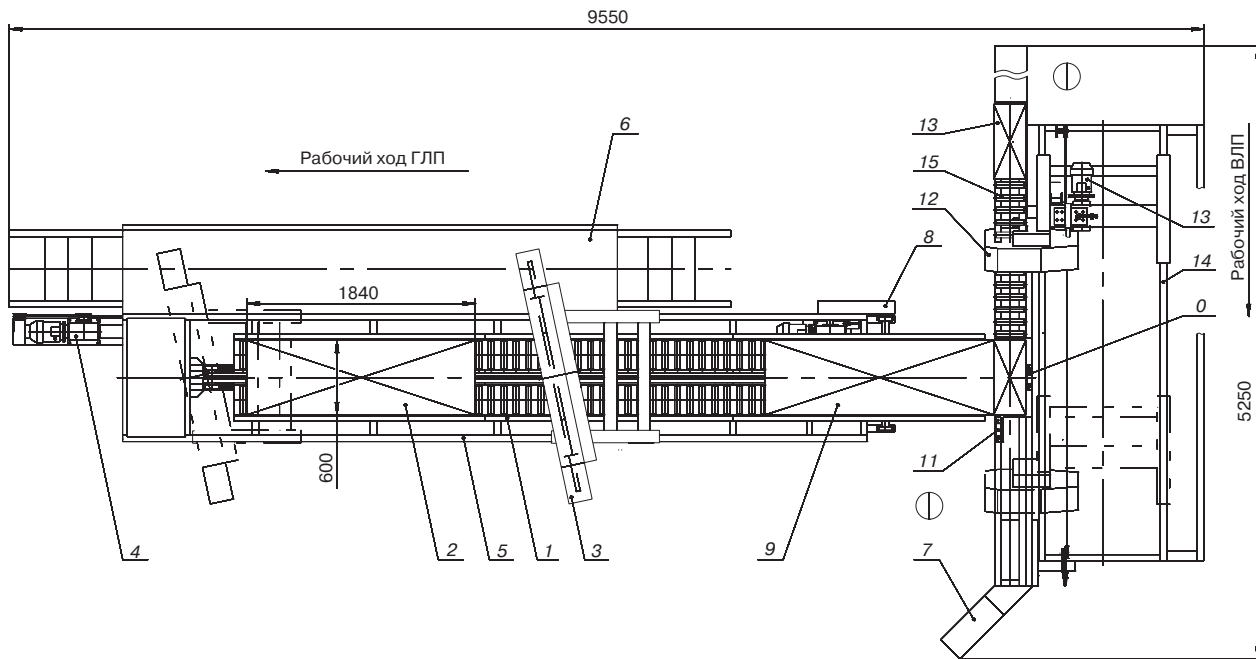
Схема комплекса резки пеноблоков ШЛ 444: 1 – рольганг; 2 – блок пенобетона; 3 – горизонтальная ленточная пила (ГЛП); 4 – привод перемещения ГЛП; 5 – рельсовый путь ГЛП; 6 – площадка обслуживания; 7 – пульт управления; 8 – привод упора подачи заготовки; 9 – блок пенобетона; 10 – упор регулируемый; 11 – упор выдвигной; 12 – вертикальная ленточная пила (ВЛП); 13 – привод перемещения ВЛП; 14 – рельсовый путь ВЛП; 15 – рольганг ВЛП
